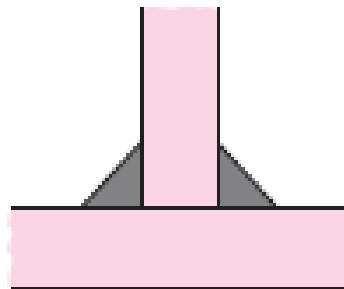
Geometría de la Soldadura tipo filete.
